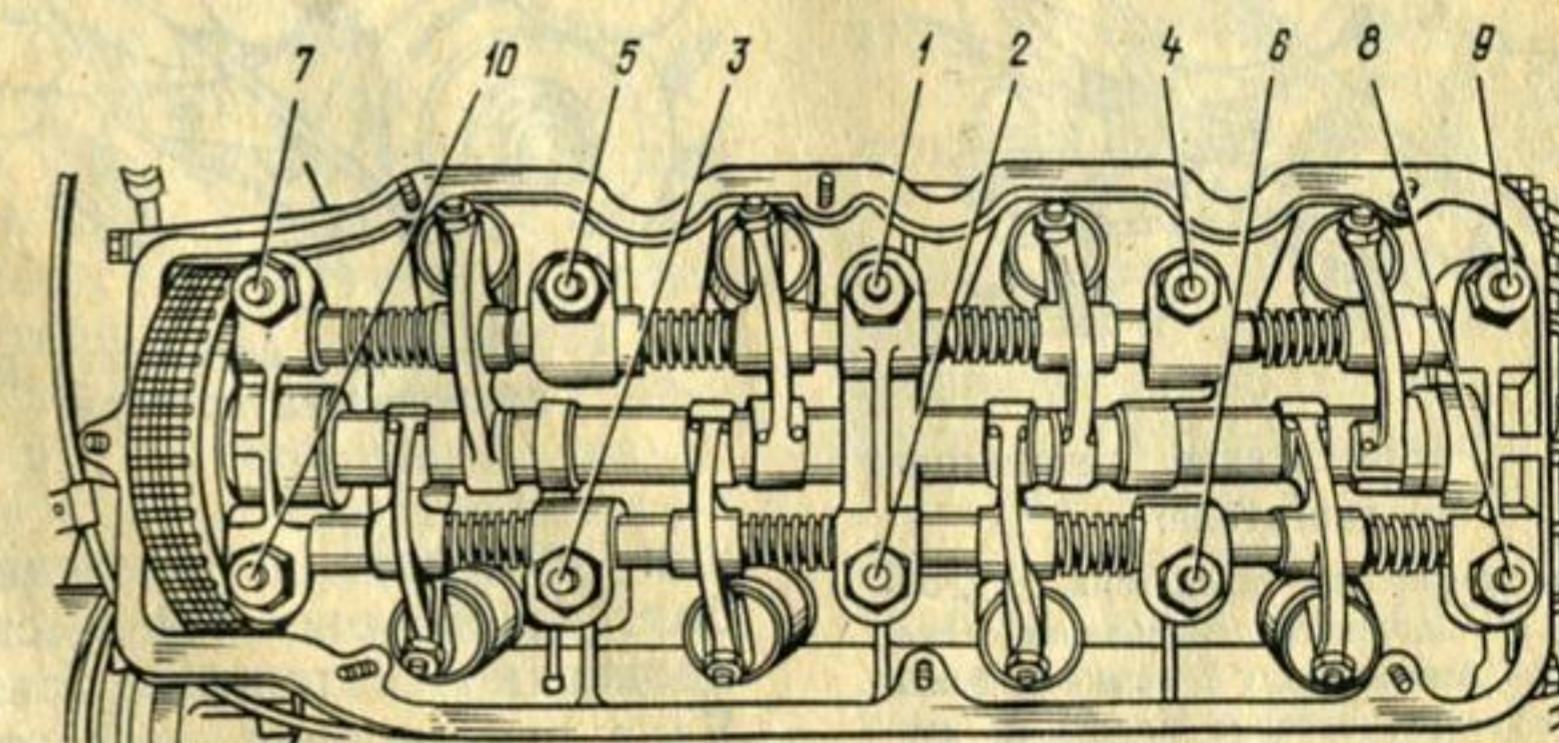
Порядок затяжки гаек шпилек крепления головки блока цилиндров к блоку
